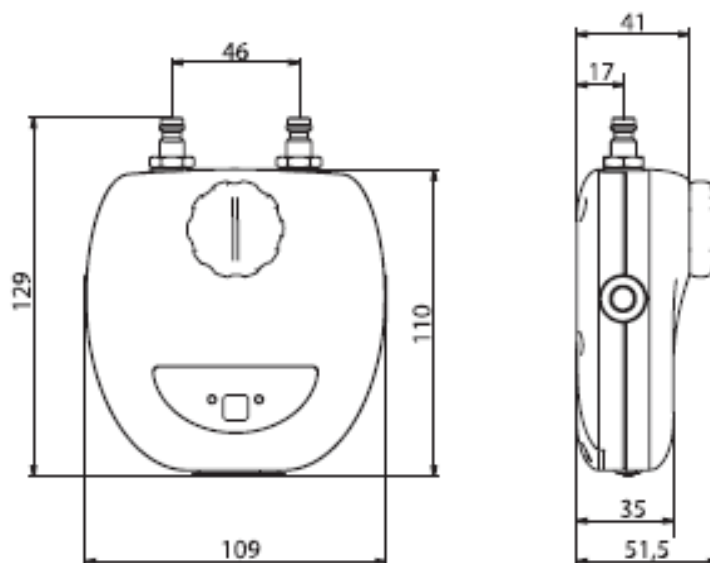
Габаритные размеры измерительного блока PFM 5000 Standard
